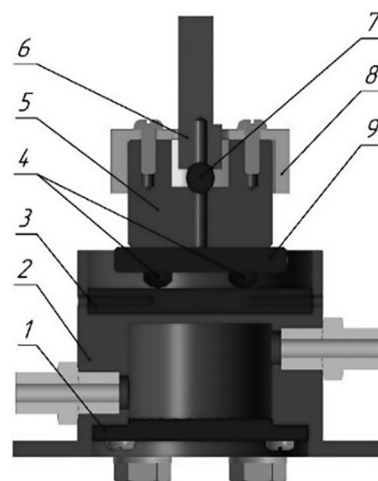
Схема узла трения: 1 — крышка основания; 2 — основание; 3 — контргело; 4 — образец; 5 — переходник; 6 — вращатель; 7 — шарик; 8 — крышка вращателя; 9 — держатель образцов
